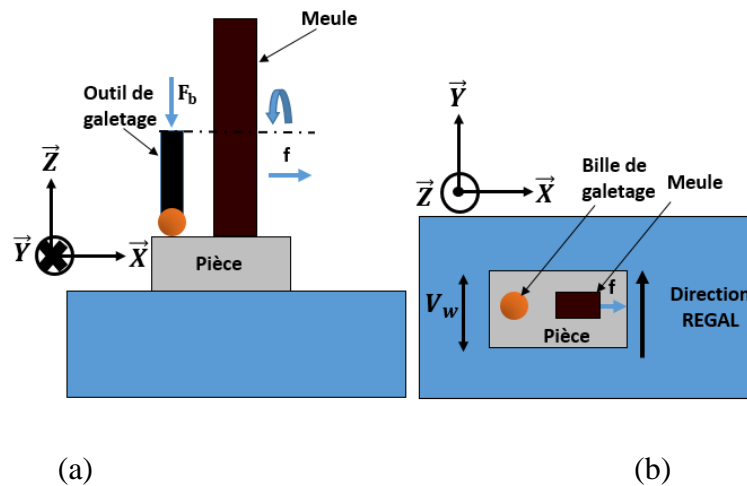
(a) Vue de face, (b) vue de dessus du procédé REGAL.
